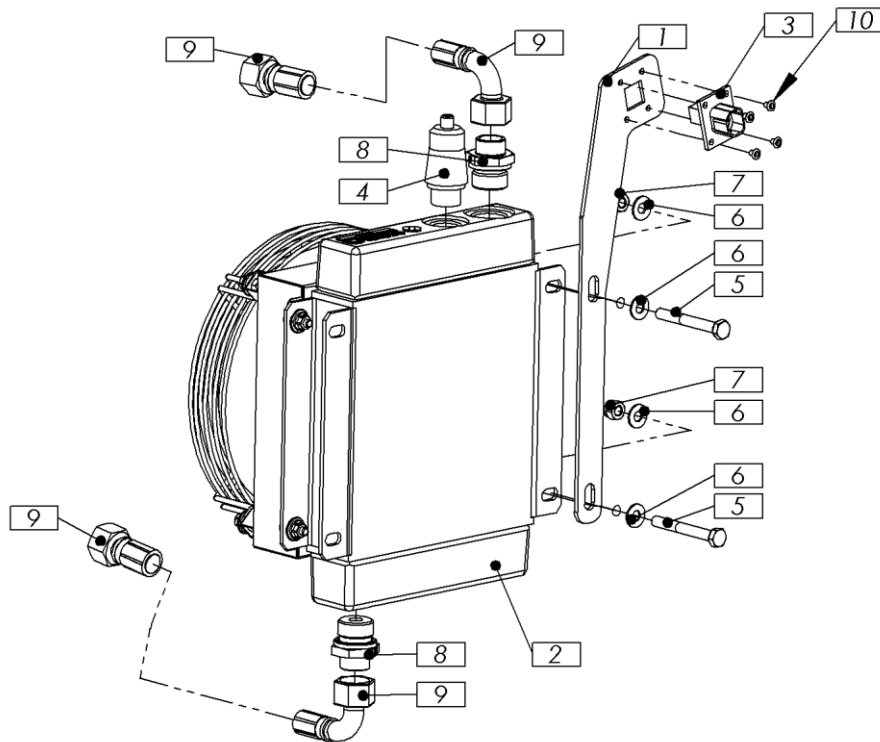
900.06.150.0 / 900.06.160.0 - Cooler kpl.
